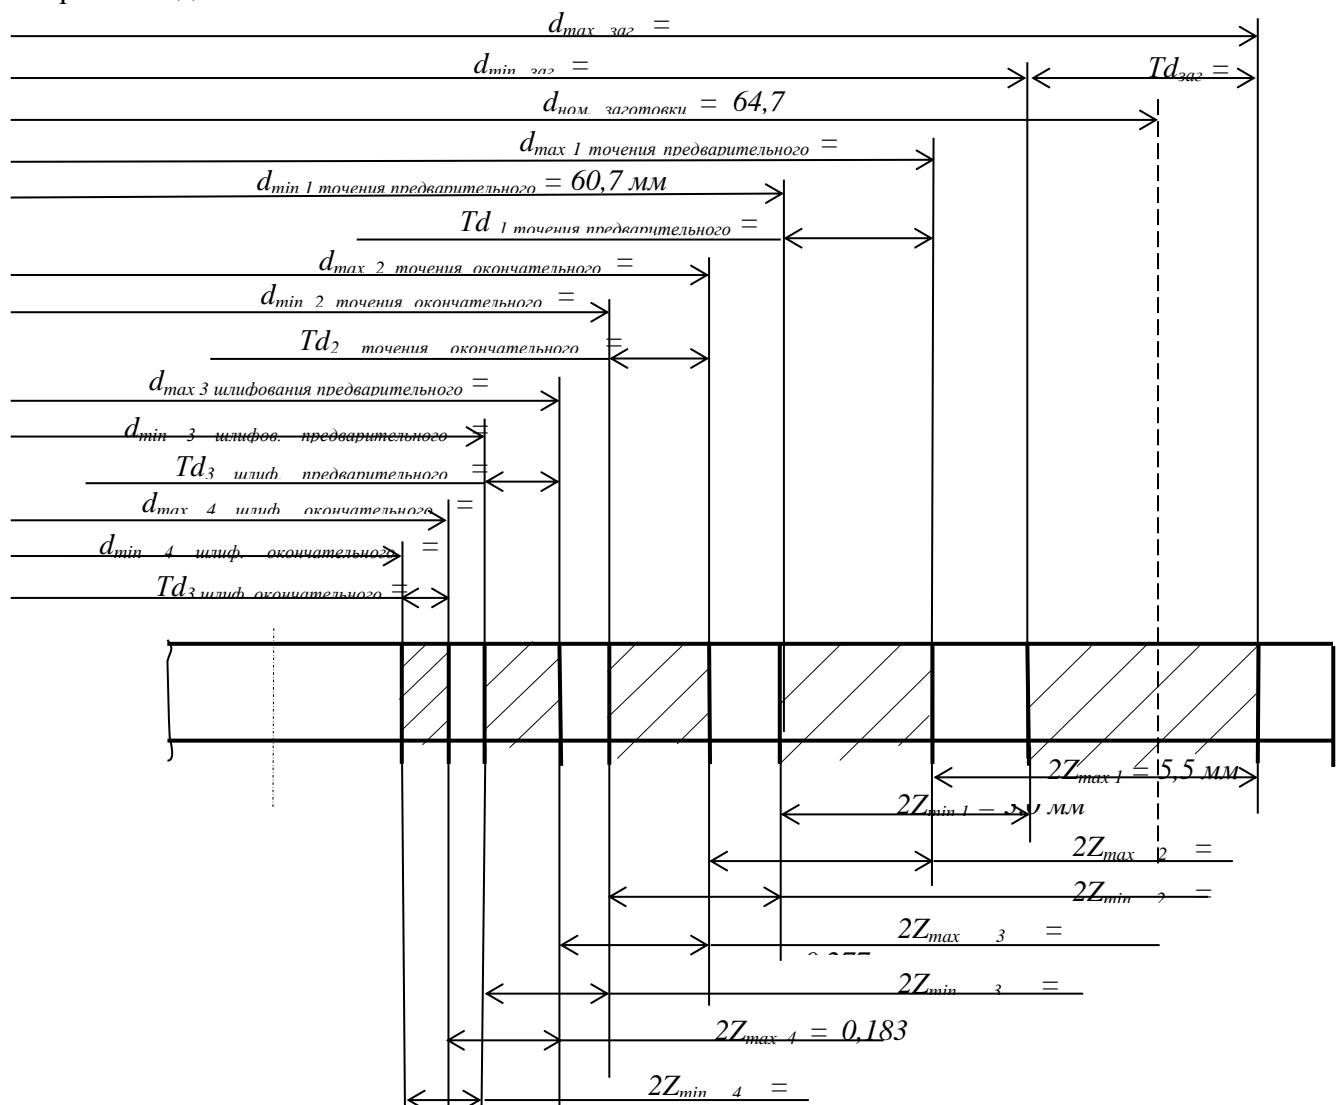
Схема расположения припусков, размеров и допусков вала
